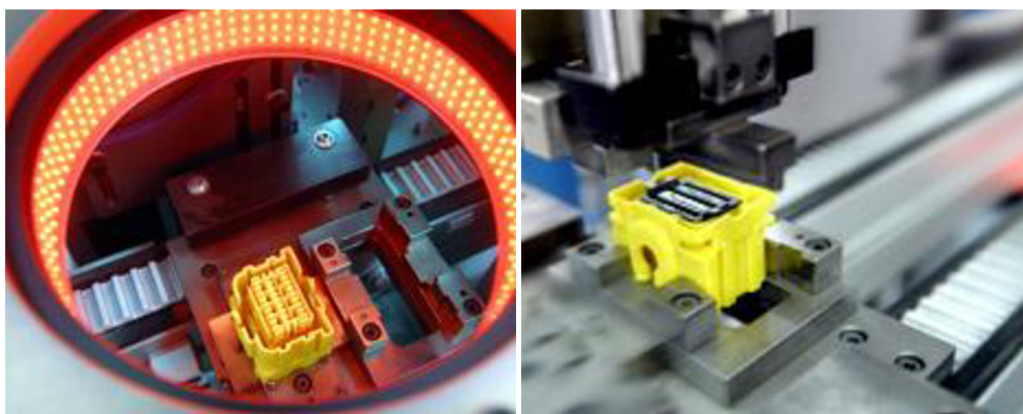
Funkce oken u přídržovačů umožňující průchod pinů.
